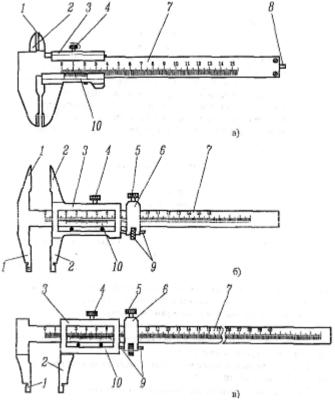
Штангенциркули: а - ШЦ I; б – ШЦ II; в - ШЦ III; 1 - неподвижные губки; 2 – подвижные губки; 3 - рамка; 4 - зажим рамки; 5 - зажим рамки микрометрической подачи; 6 - рамка микрометрической подачи; 7 - штанга; 8 - линейка глубиномера, 9 - винт и гайка микрометрической подачи; 10 – нониус
